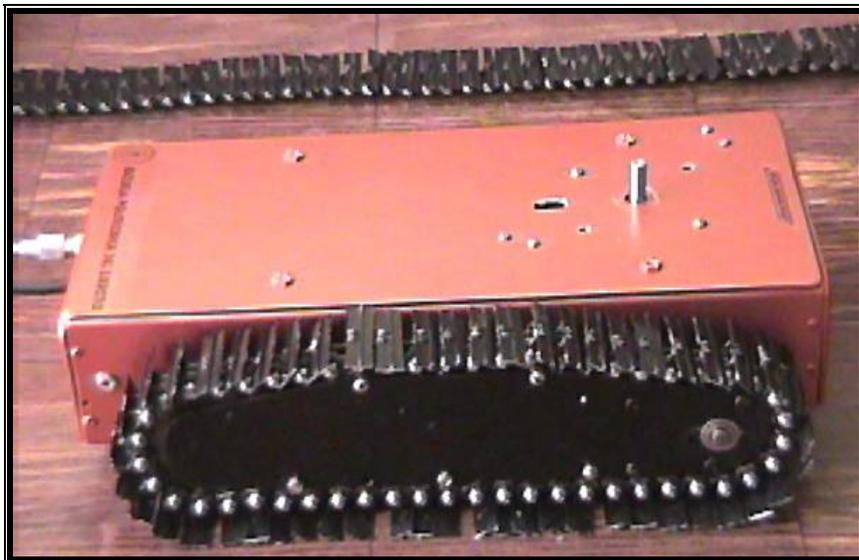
Montaje de la Cadena con Zapata del Lado Derecho
